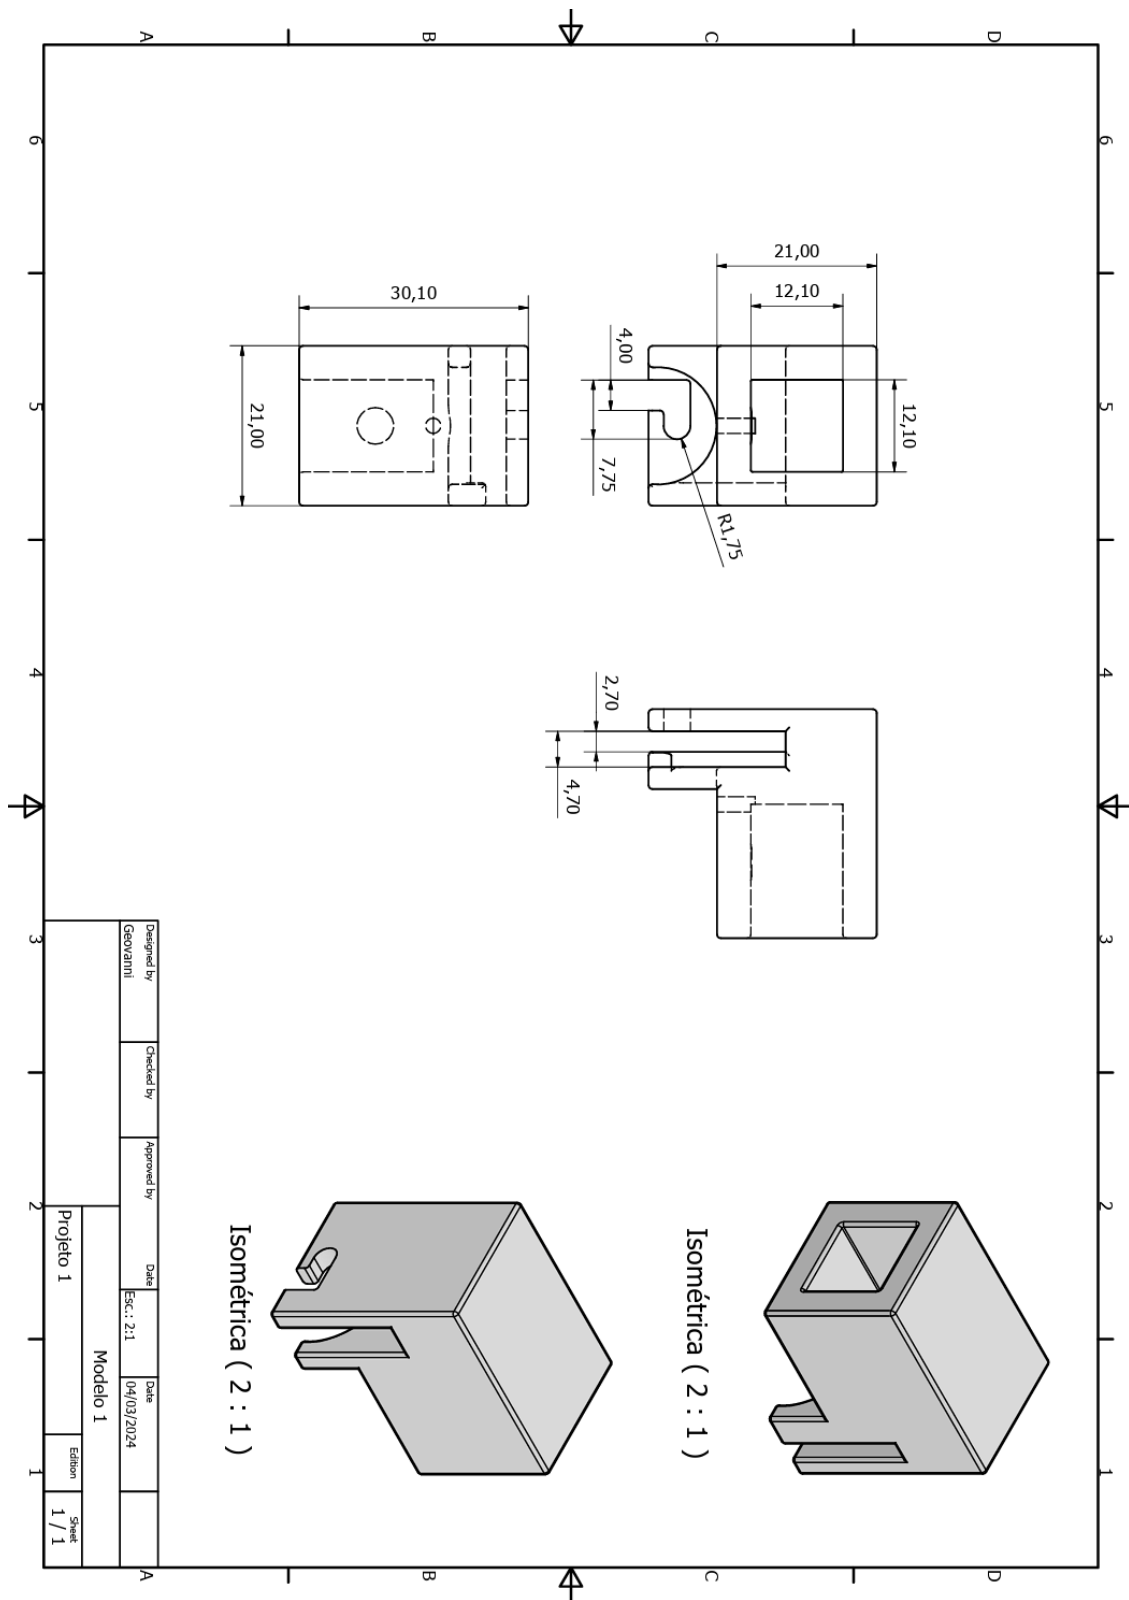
Modelo Final Adaptador Do LASER Para Impressora 3D
